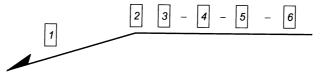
Структура условного обозначения сварного шва:
